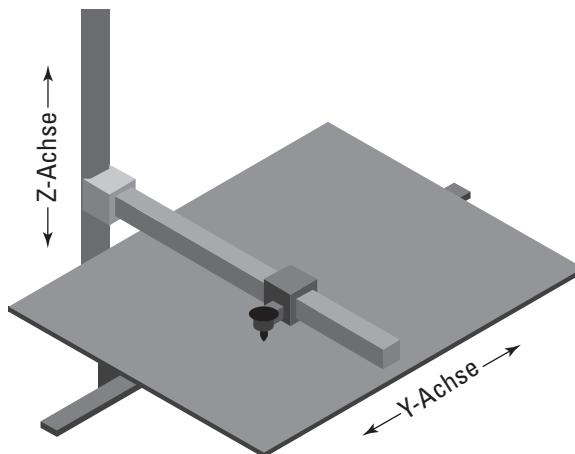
Ein 3D-Drucker im kartesischen Stil, der Objekte erzeugt, indem er seinen Extruder (das heiße Ende) in drei Dimensionen bewegt
